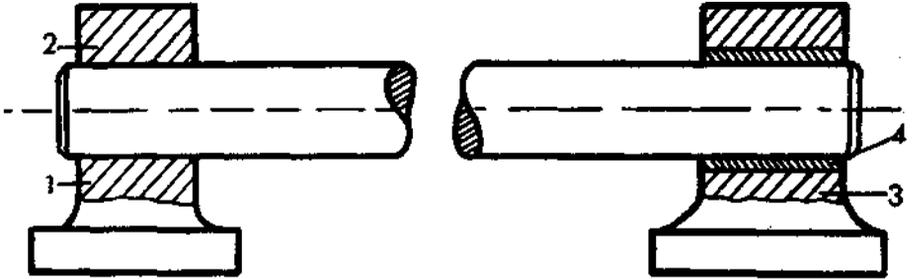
Soportes de un eje que gira. —1. Soporte de fundición. —2. Eje de acero. —3. Soporte de fundición. —4. Cosquillo de bronce fijo al soporte.
